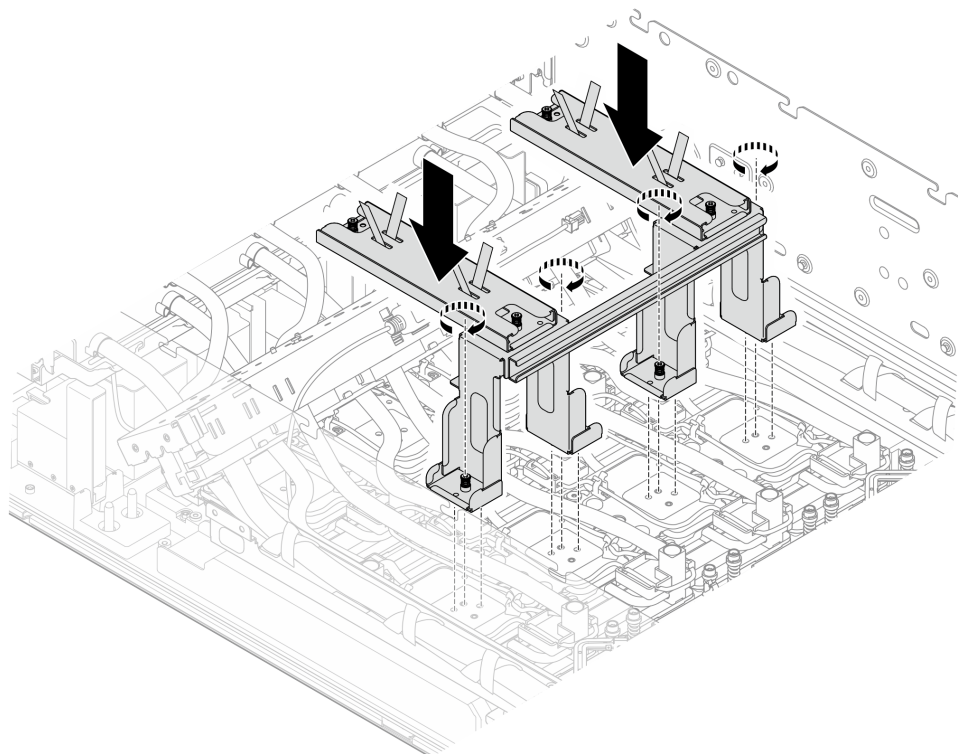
Installazione delle staffe di spedizione sulle piastre a freddo della GPU posteriore
